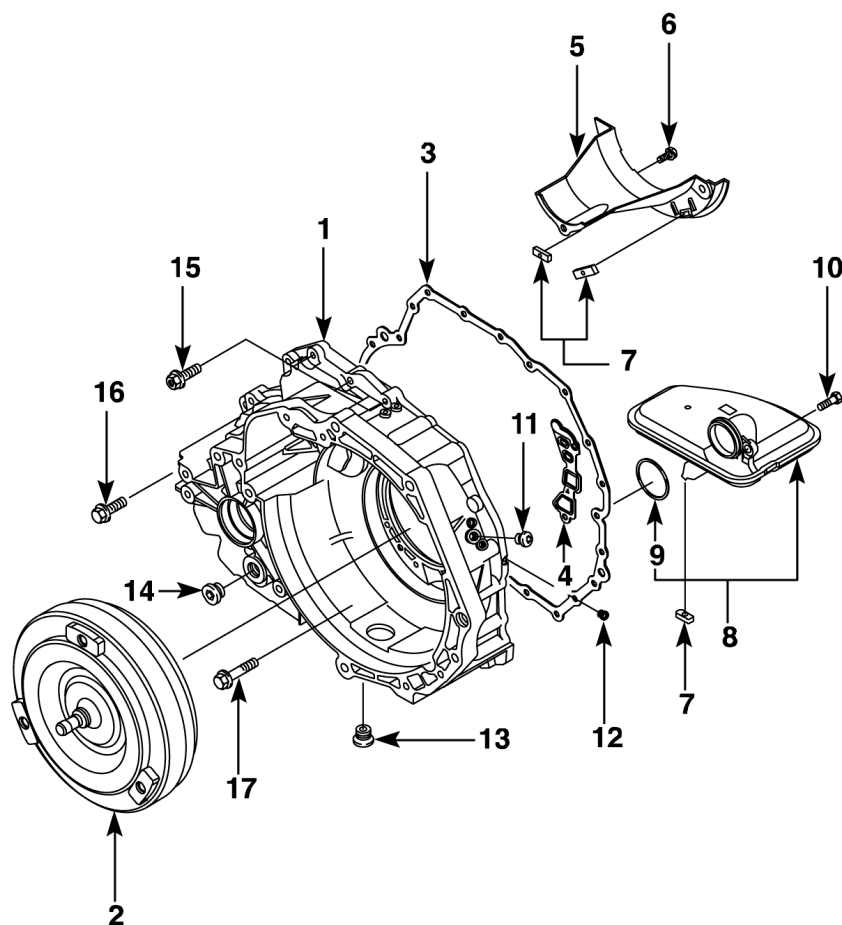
Гидротрансформатор. 1. Корпус гидротрансформатора; 2. Гидротрансформатор; 3. Прокладка; 4. Стальная прокладка; 5. Маслоотражатель; 6. Болт; 7. Магнит; 8. Масляный фильтр; 9. Кольцевой уплотнитель; 10. Винт; 11. Заглушка; 12. Заглушка; 13. Пробка сливного отверстия; 14. Пробка уровня масла; 15. Винт; 16. Болт; 17. Болт.
